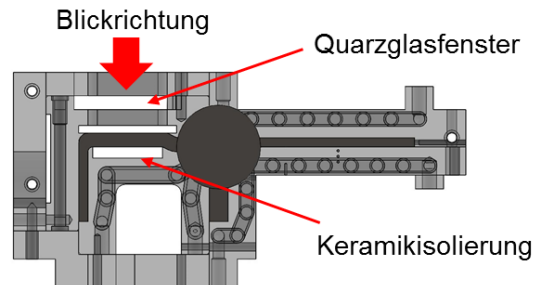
Modularer Kokillenaufbau, erweitert um Module zur Erzeugung eines „Hotspots“ im Gussteil und um ein Fernster zur in-situ Videoaufzeichnung der Heißrissentstehung
